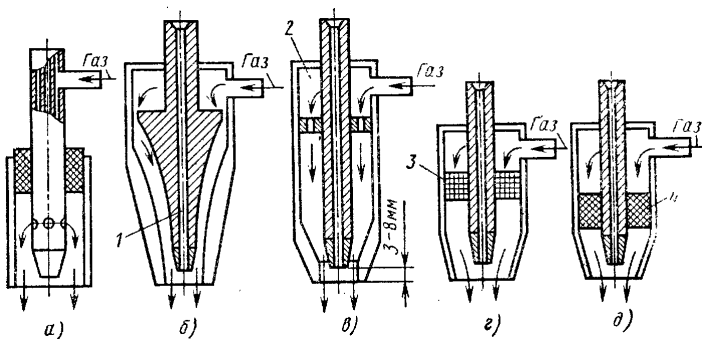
Схемы питания газом сварочных горелок
